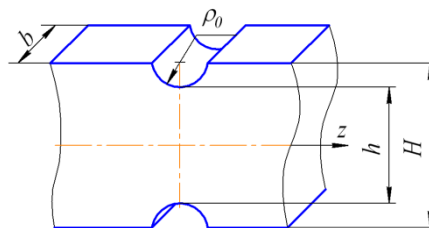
Рабочая часть детали прямоугольного поперечного сечения для испытаний на усталость
